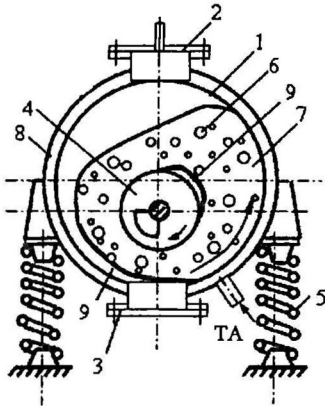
Вибрационная сушилка-мельница: 1 - корпус; 2, 3- крышка загрузочного и выгрузочного люков; 4- вибратор; 5- упругие опоры; 6- мелющие тела; 7- обрабатываемый материал; 8- теплообменная рубашка; 9 - серповидные зазоры; ТА - телловой агент.
